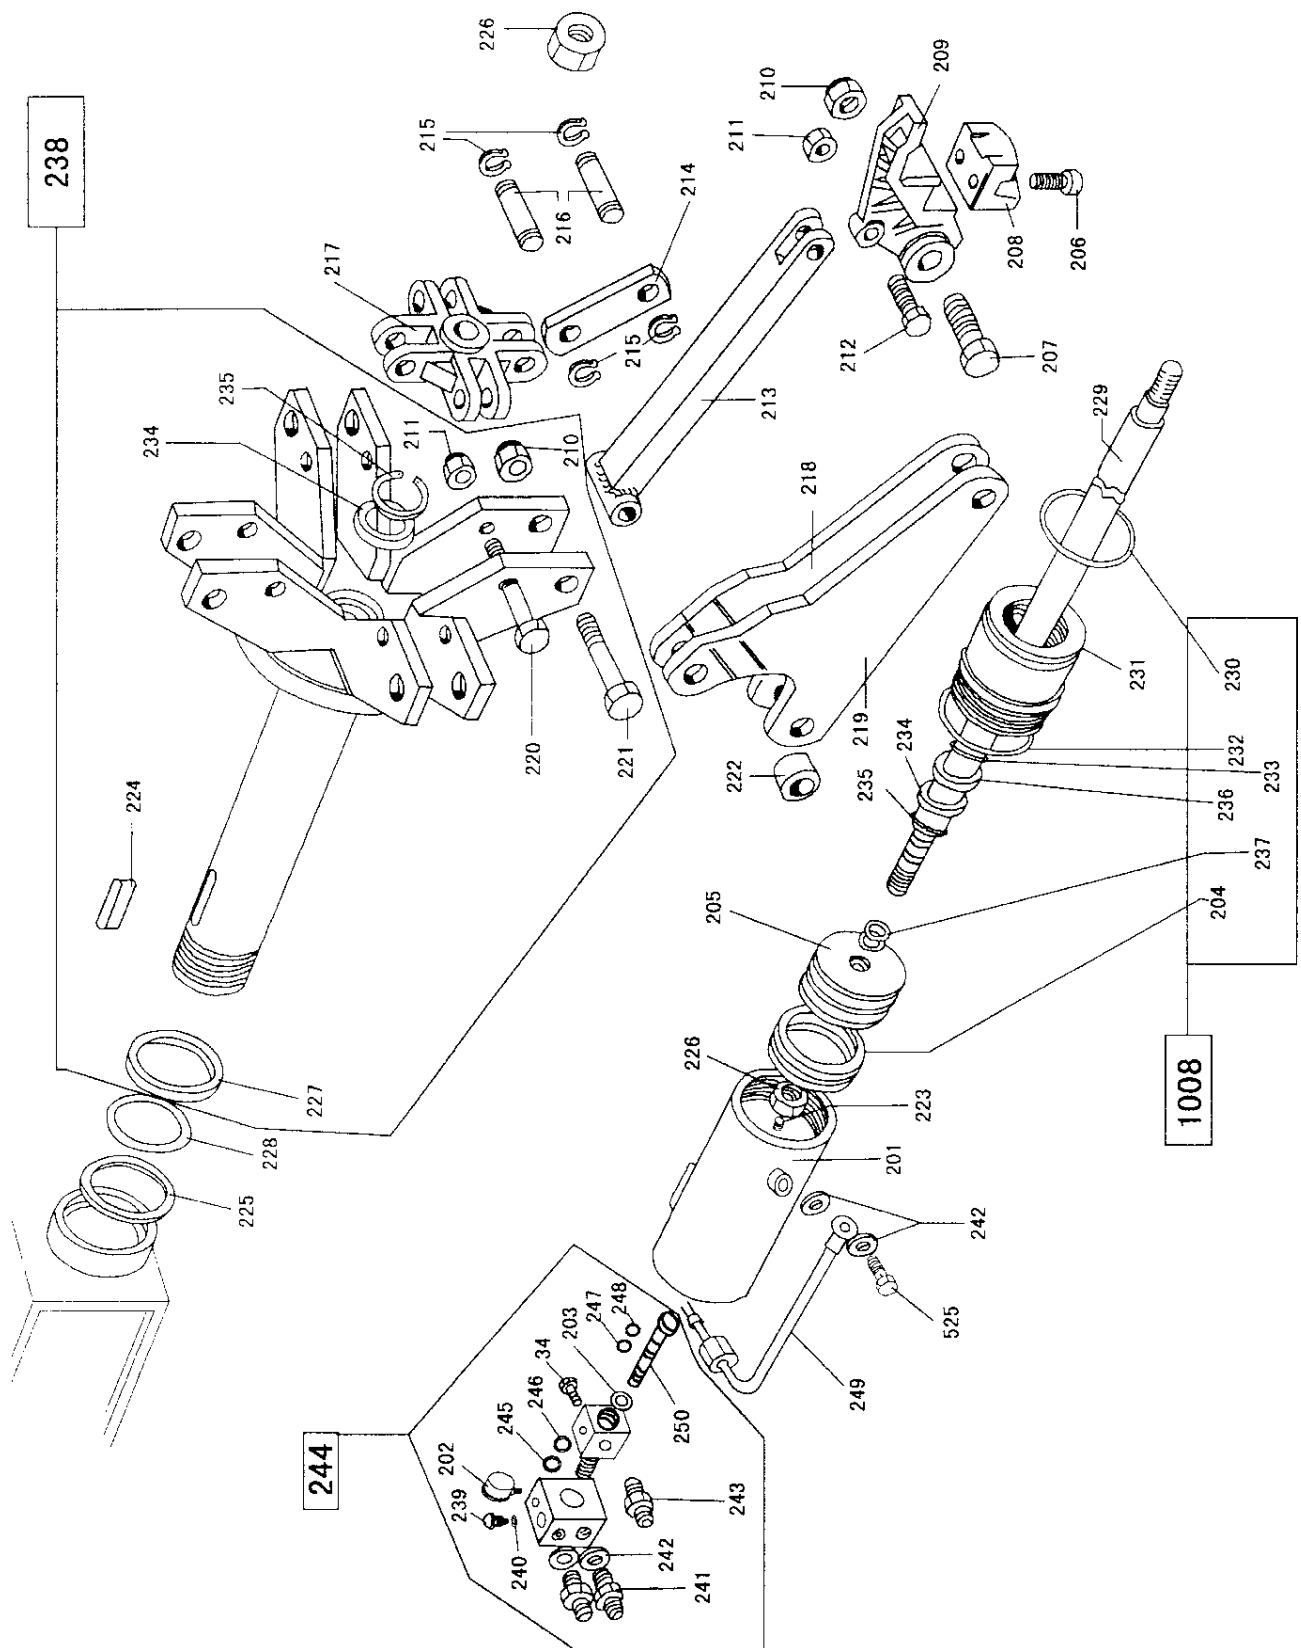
GETRIEBE-GEARBOX-REDUCTEUR
